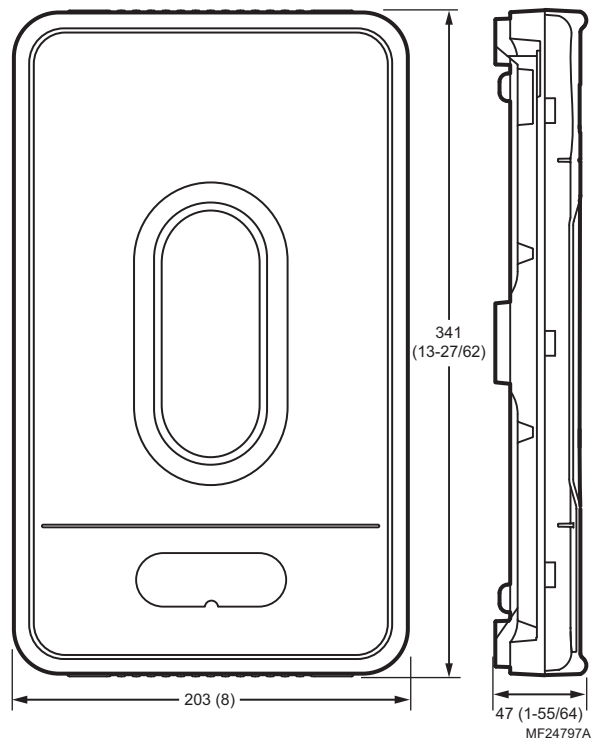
Dimensions du panneau de zone TAZ-4H en millimètres (pouces).
